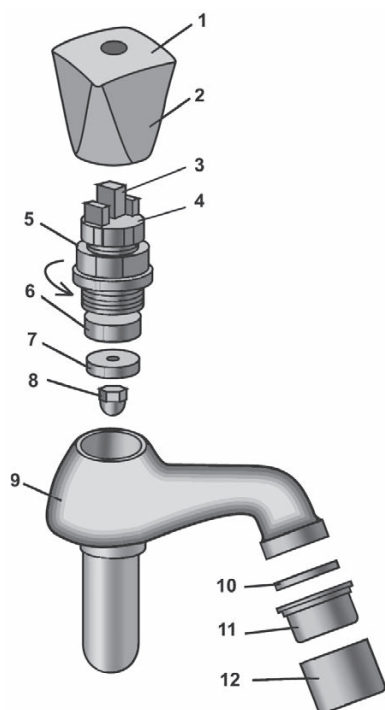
Конструкция водопроводного крана: 1 — пластмассовый колпачок; 2 — ручка; 3 — четырехгранный со шпинделем; 4 — сальник; 5 — корпус вентиля со шпинделем; 6 — пластина вентиля; 7 — прокладочное кольцо; 8 — уплотнительная шайба; 9 — корпус крана; 10 — уплотнитель; 11 — насадка; 12 — мунштук
